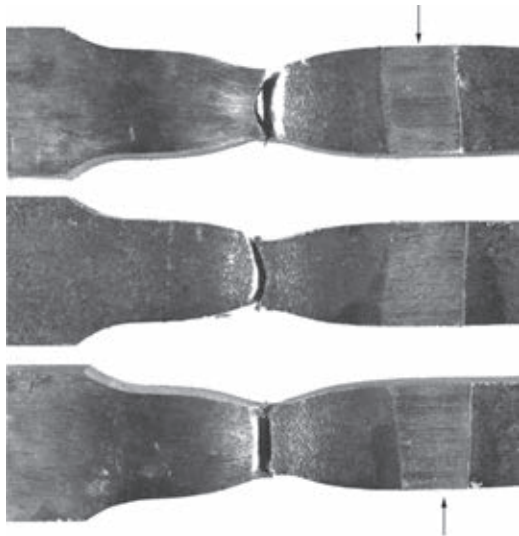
Стандартные образцы, испытанные на растяжение. Все разрушения произошли по основному металлу. Стрелками показана ЗС
